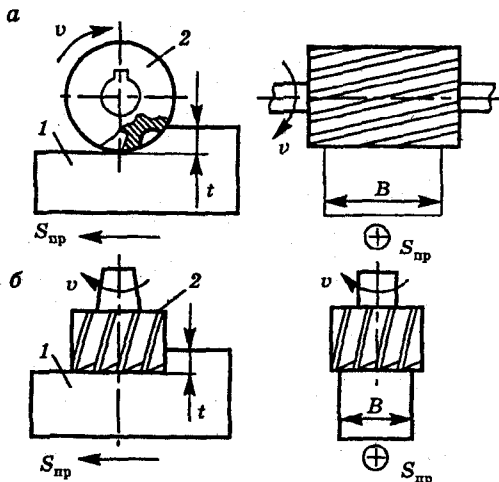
Фрезерование цилиндрической (а) и торцевой (б) фрезами:
